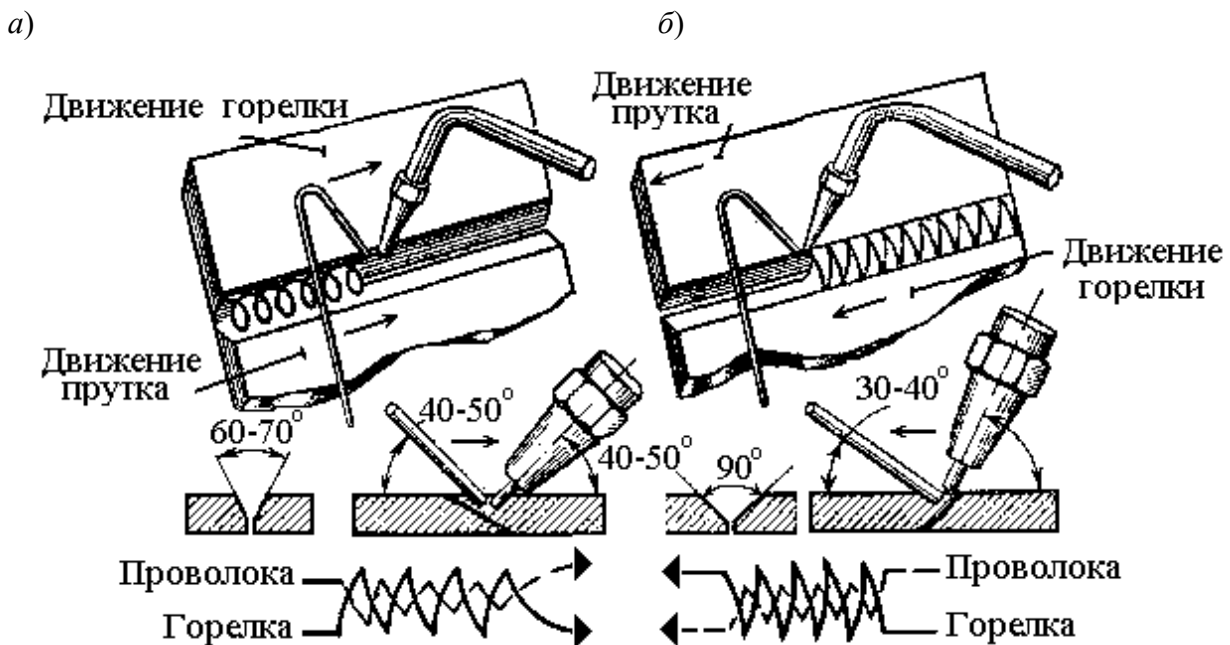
Правый (а) и левый (б) способы газовой сварки
